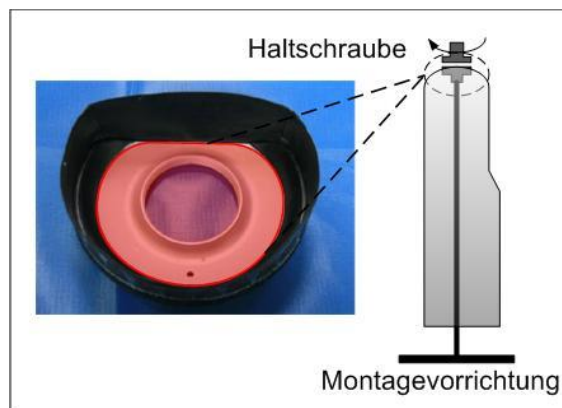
Installation der Halteschraube. Das freiliegende Aluminium (rot markiert) wird durch die Haltschraube abgedeckt.
